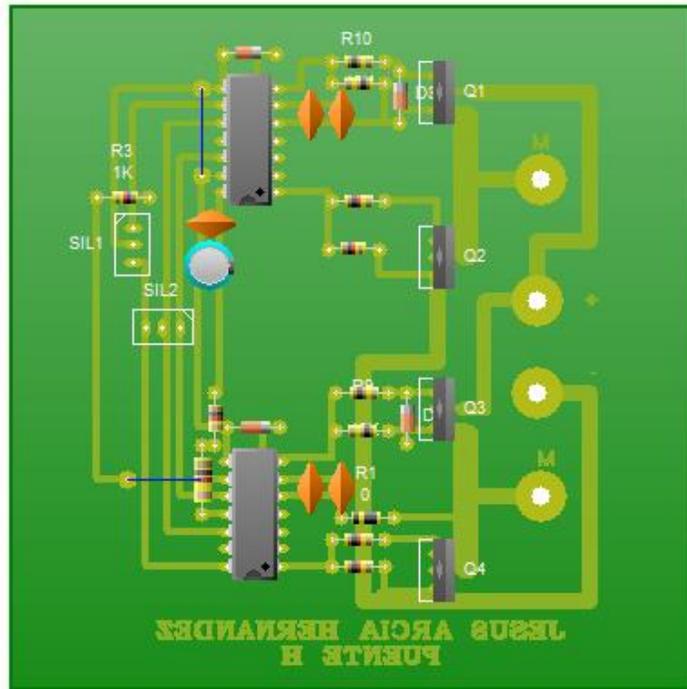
, esquemático pcb 2D puentes h, fuente autor.
